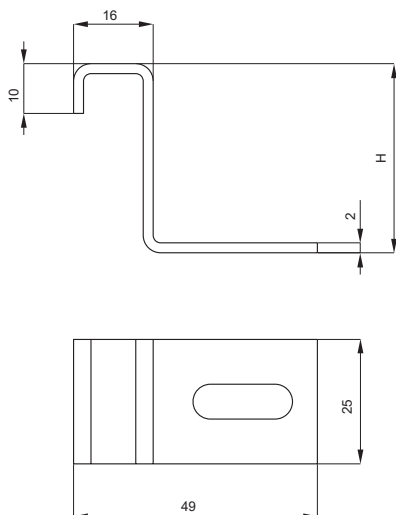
Скоба для крепления лотка / Figure B.1 – C-clamp for cable tray
